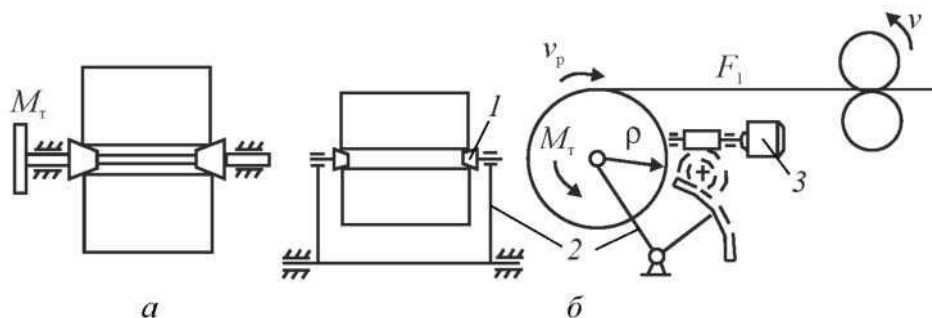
Схемы рулонных установок: а - шпиндельная установка; б - бесшпиндельная установка: 1 - консольный вал; 2 - поворотный рычаг; 3 - электродвигатель
